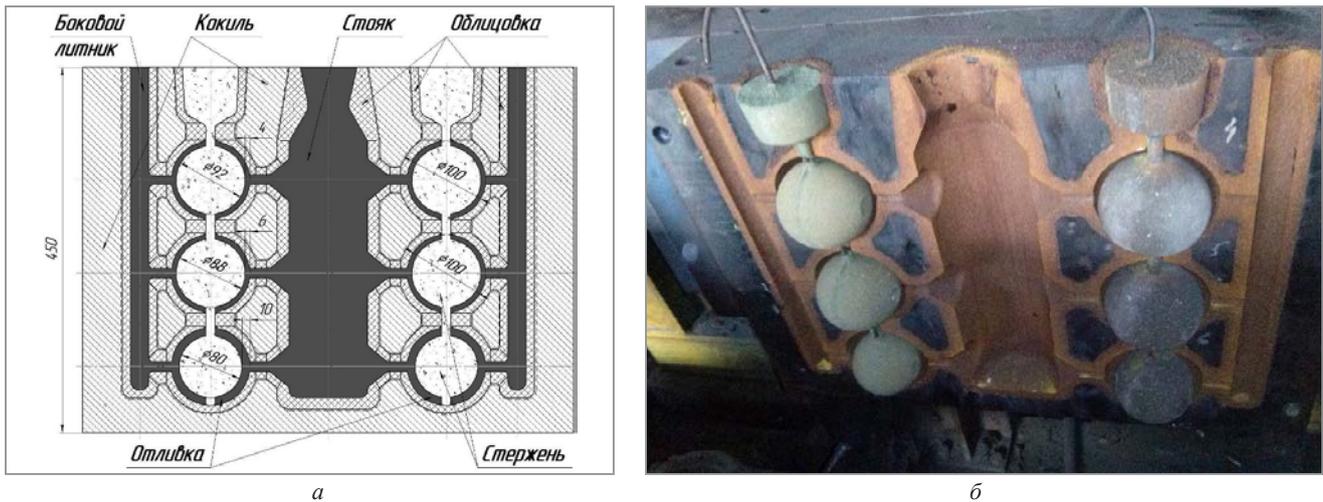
Технологическая схема простановки стержней в облицованном кокиле для проб-отливок с толщиной стенок 10 мм, 6 и 4 мм (а); облицованный кокиль с универсальной литниковой системой для получения стержневых проб-отливок в виде полых шаров с прилитыми образцами и простановка стержней из ХТС в облицованном кокиле (б)
